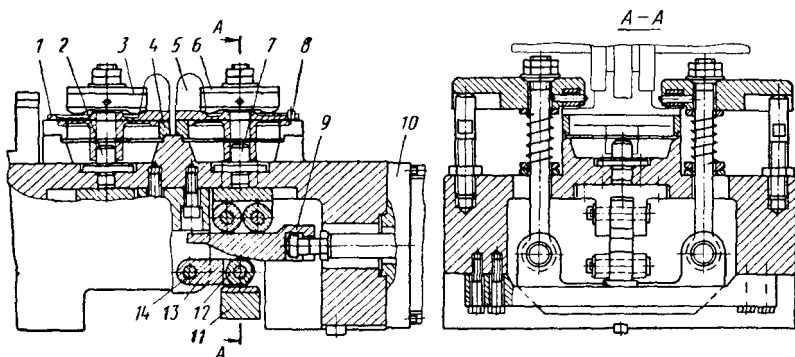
Двухместное приспособление для крепления корпусных деталей при фрезеровании П-образного выступа
